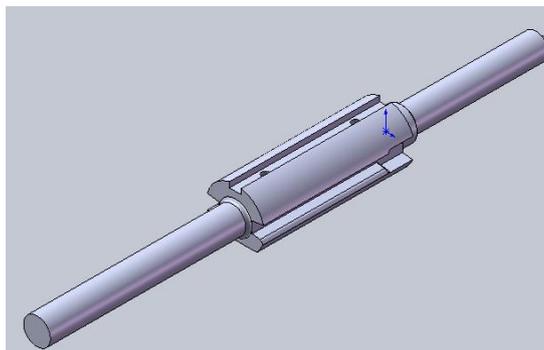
Dibujo en SolidWorks del Eje de Mandril
